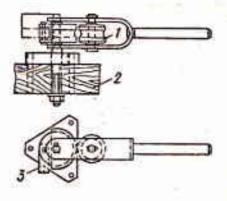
Ручной трубогиб СТВ: 1 — поворотный ролик; 2— доска верстака;
